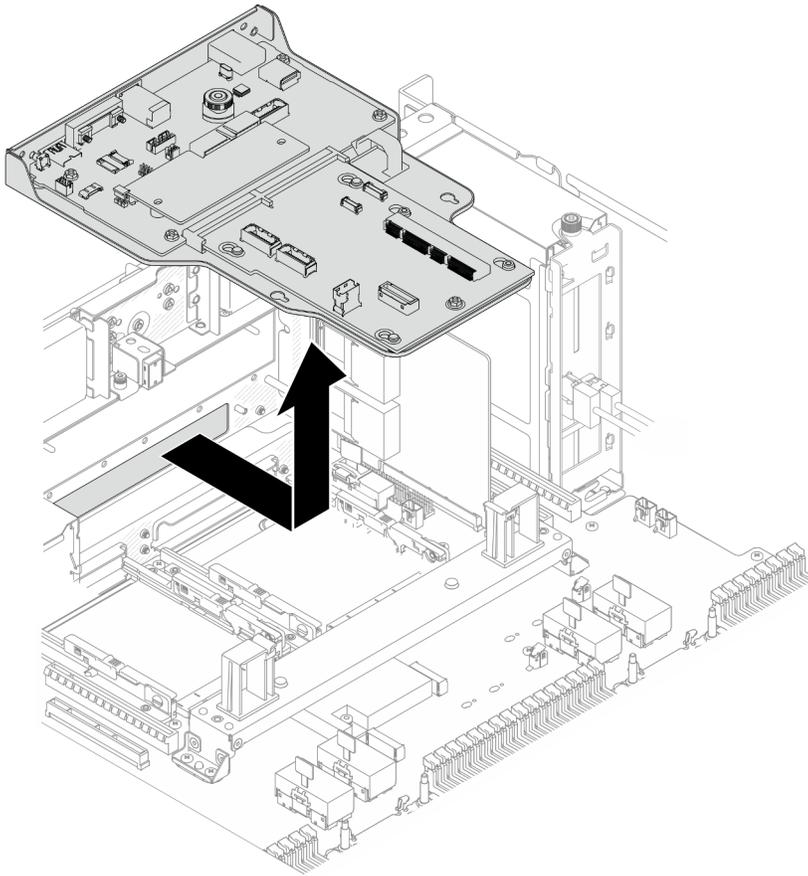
Entfernen der System-E/A-Platinen- und Interposer-Platinenbaugruppe
